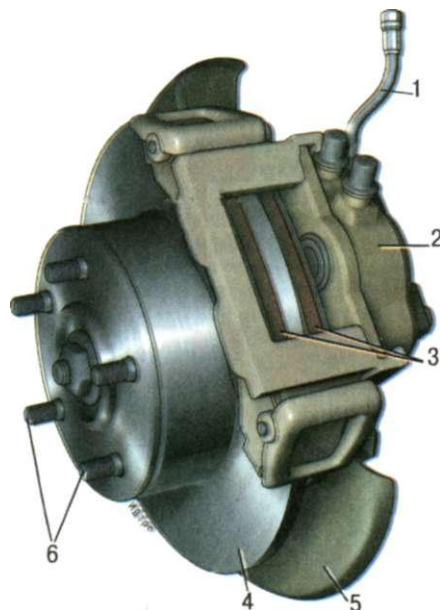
Дисковый тормозной механизм: 1 - тормозной шланг; 2 - колесный тормозной цилиндр; 3 - тормозные колодки; 4 - тормозной диск; 5 - защитный кожух; 6 - шпильки для крепления колеса
